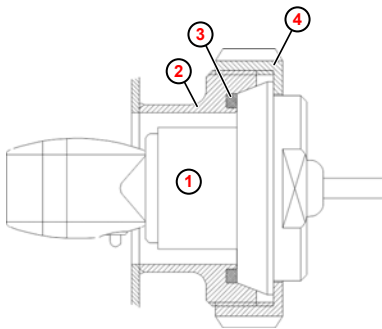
Tankwandeinbau mit Anschweißarmatur
